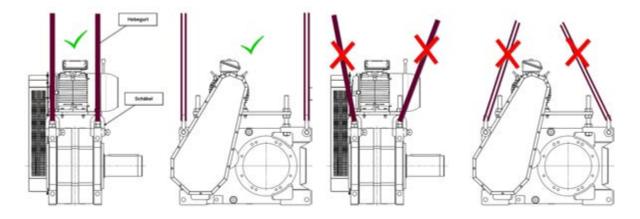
Транспортировка редуктора вместе с клиноременной передачей
